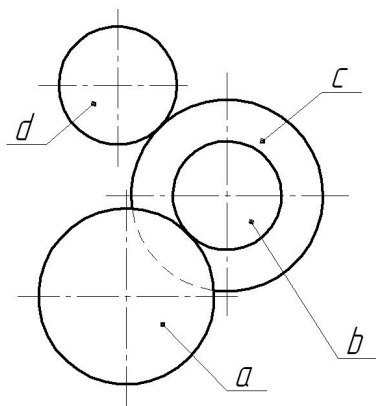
Схема расположения зубчатых колес в гитаре обката
